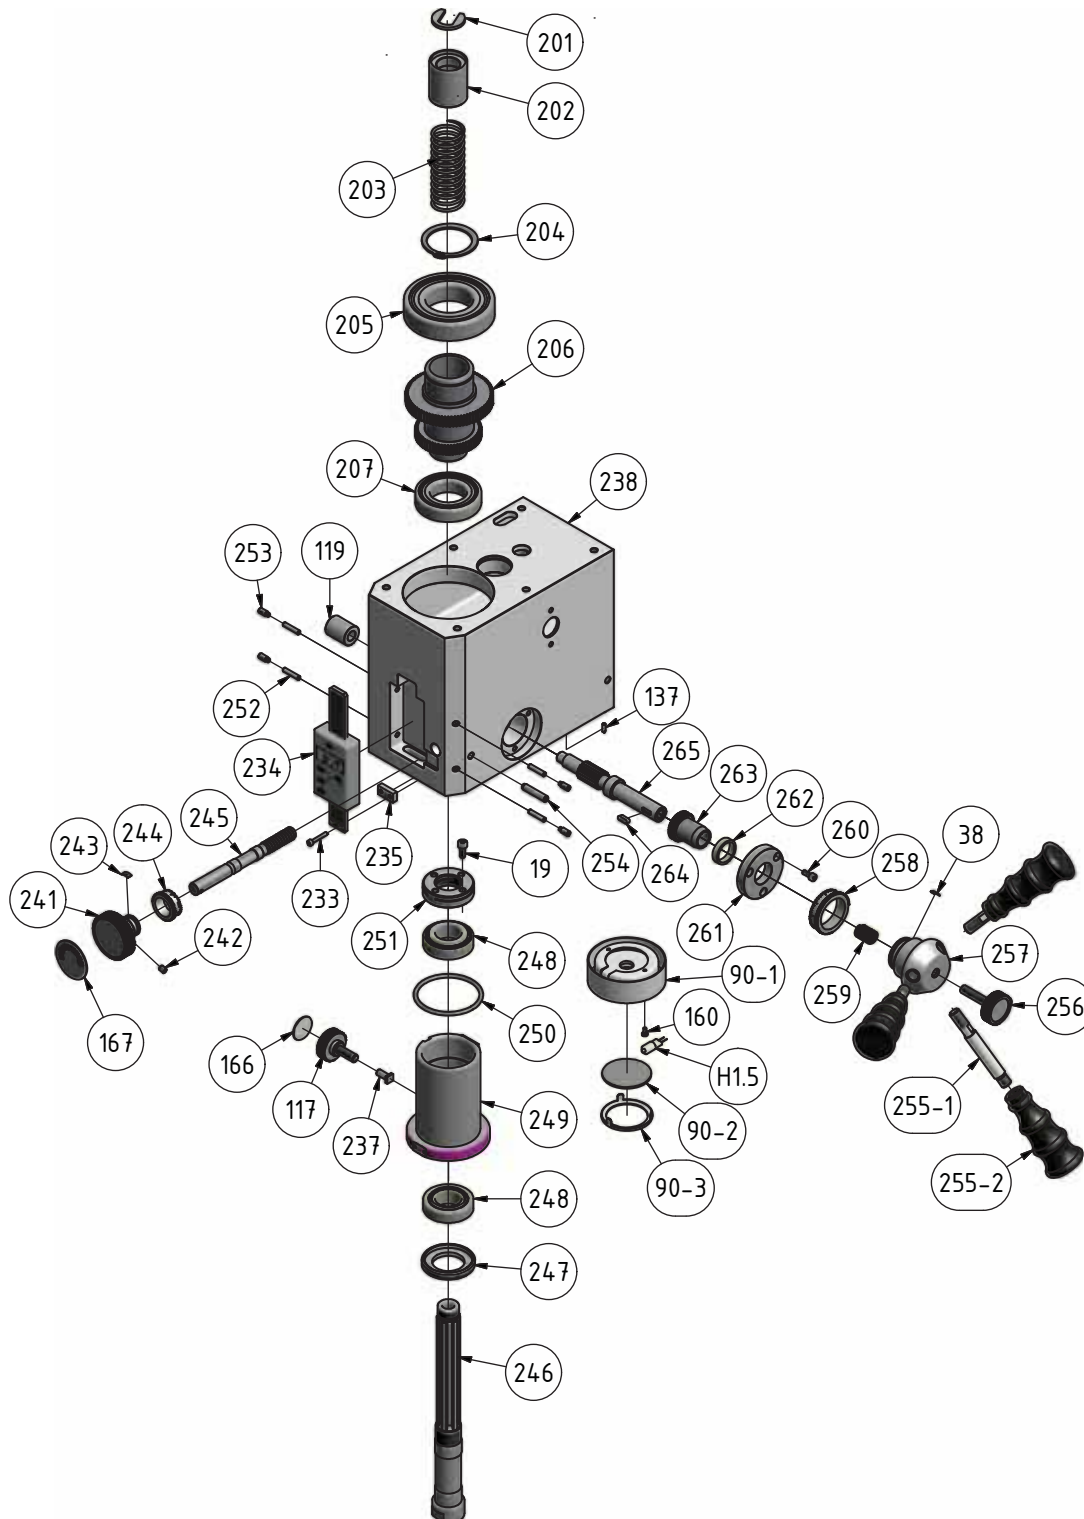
Fräskopf 2 von 2 - Milling head 2 of 2
